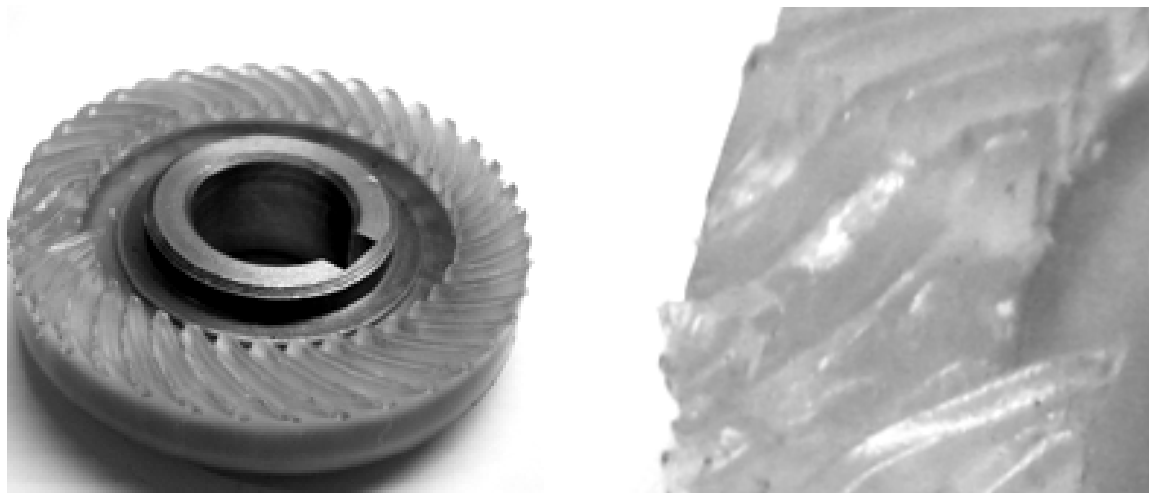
Разрушение зубьев металлополимерного спироидного колеса
